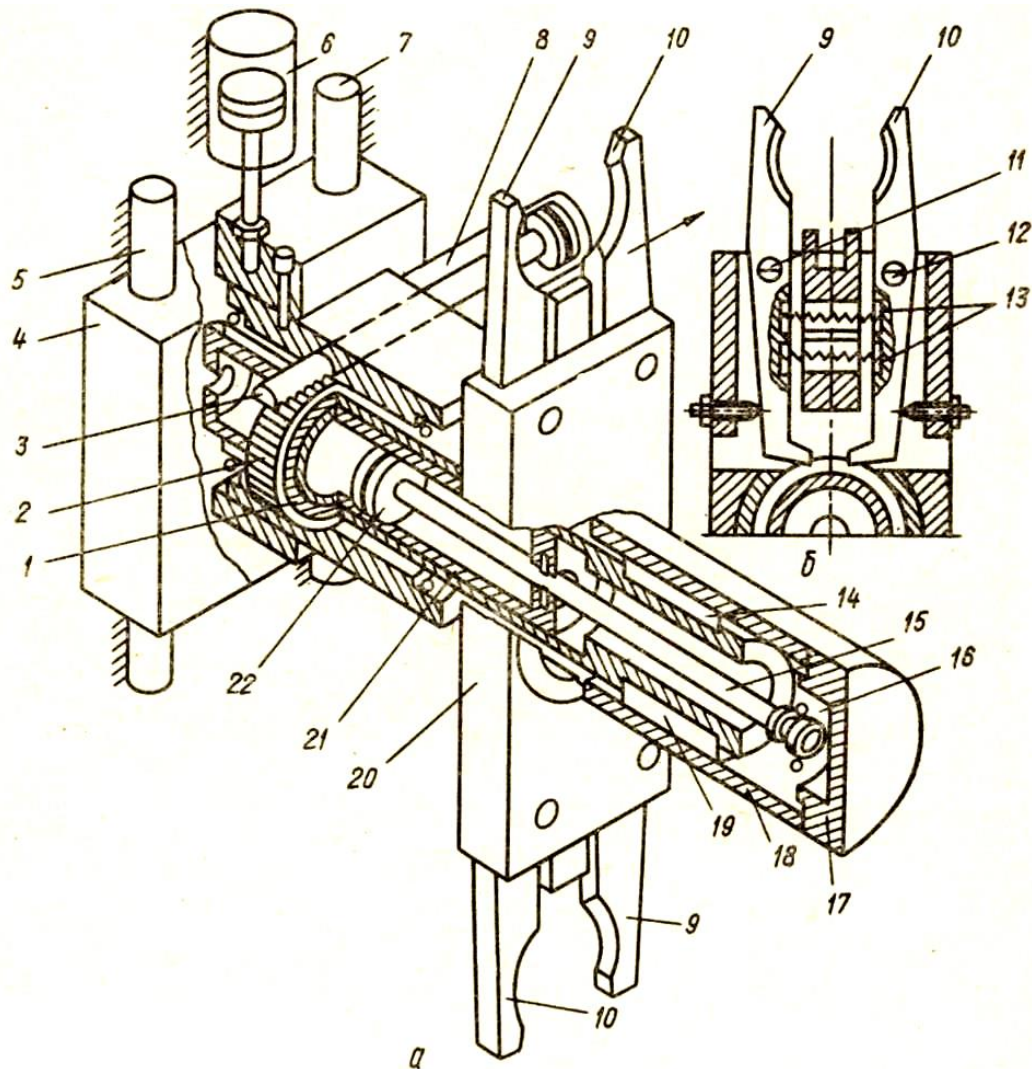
Схема автооператора для зміни інструмента на верстаті з ЧПК
